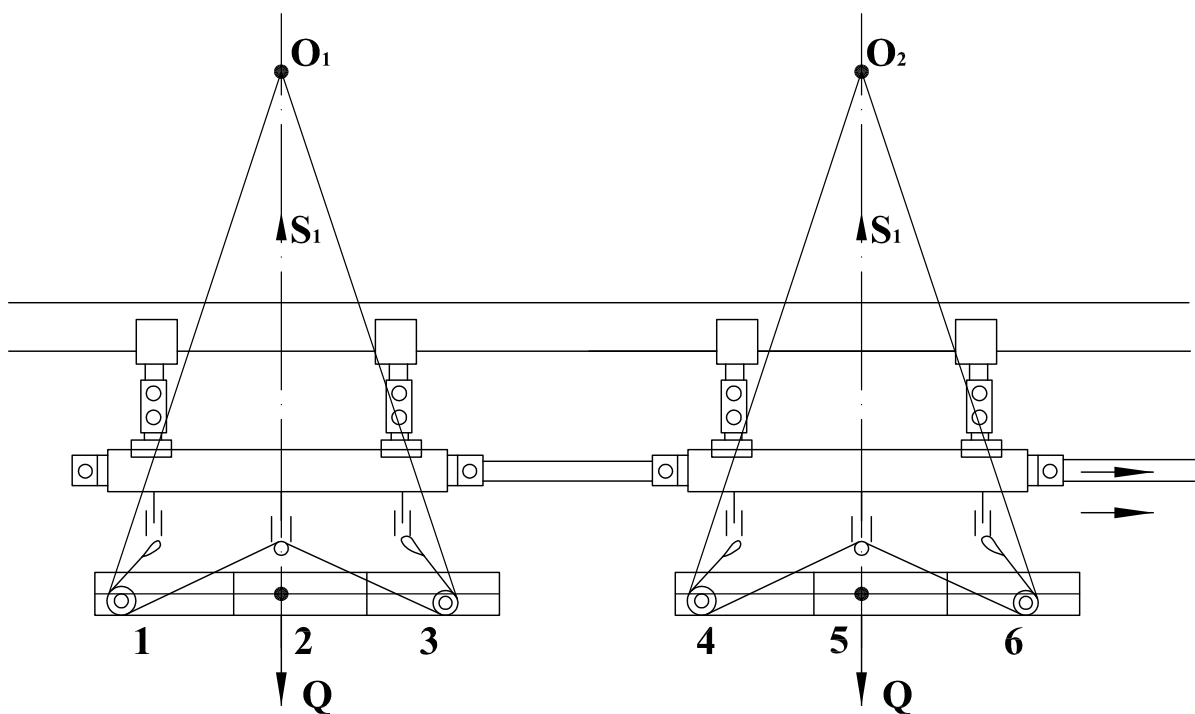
Способ строповки шести линейных секций лавного конвейера (рештаков) с включением двух гидроподъемников
